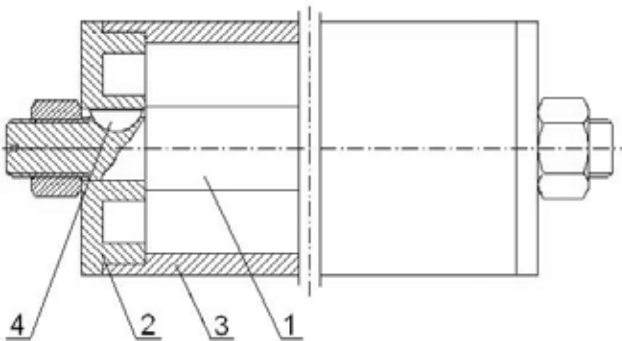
Конструкція базової циліндричної частини текстильного валика
